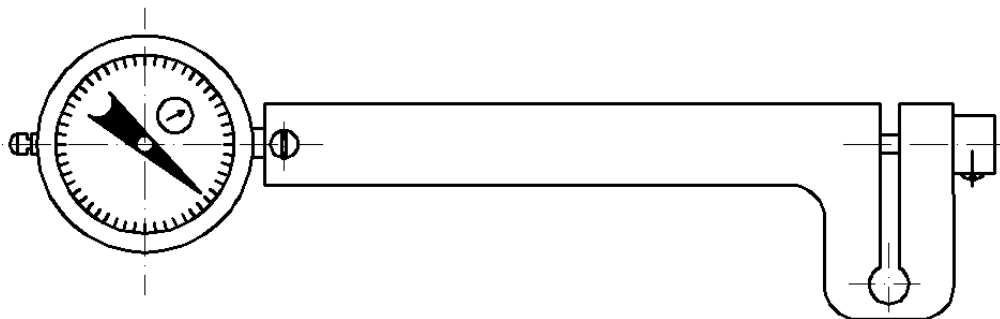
Зовнішній вигляд пружної державки для вигладжування
